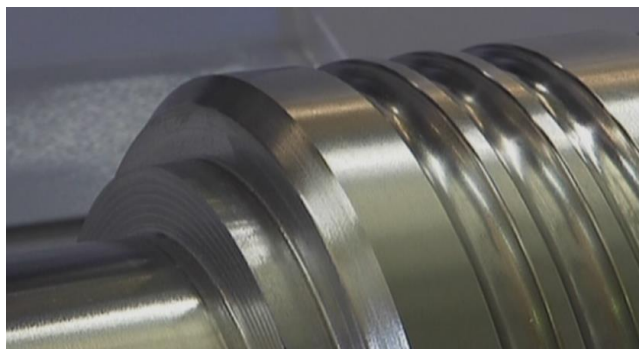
Вид бочки чистового валка после расточки калибров
